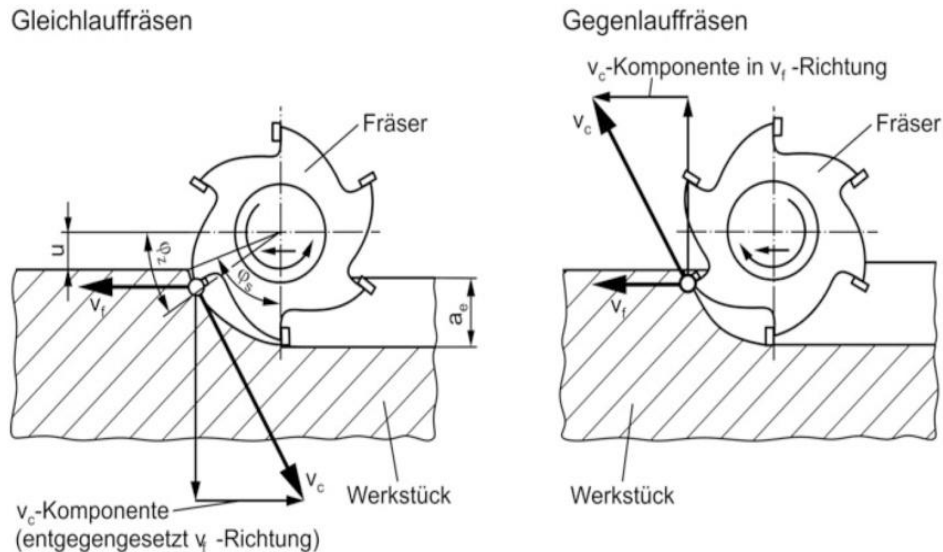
Gleich- und Gegenlauffräsen; Quelle: Werkzeugmaschinen Aufbau, Funktion und Anwendung von spanenden und abtragenden Werkzeugmaschinen, Springer
